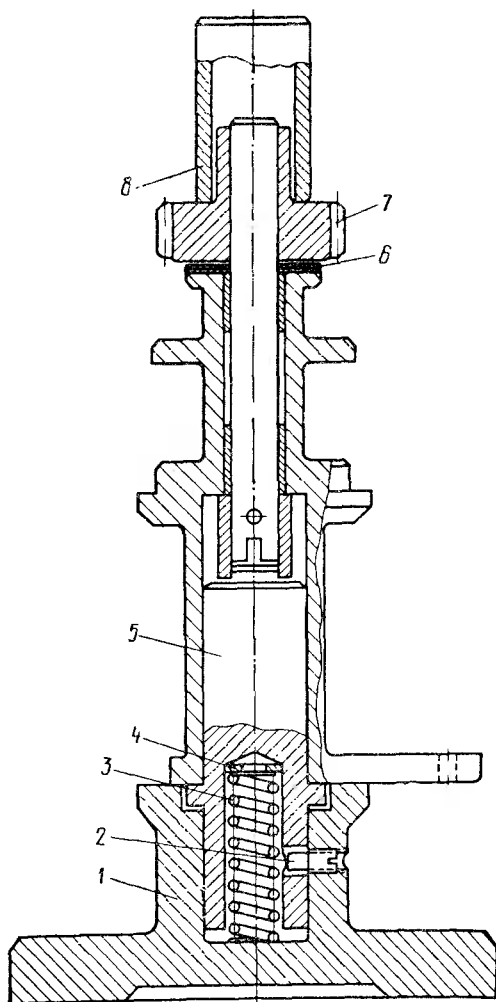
Приспособление для сборки привода прерывателя-распределителя:
